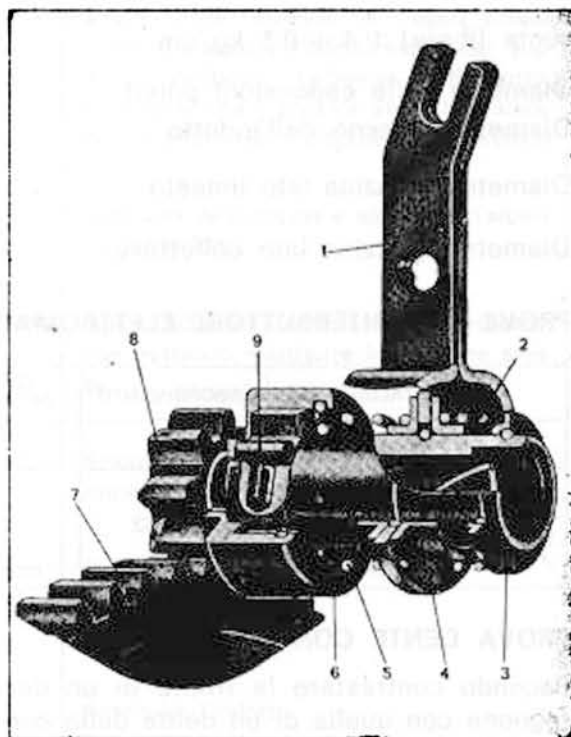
Sezione del dispositivo d'innesto combinato a spinta e ad elica
